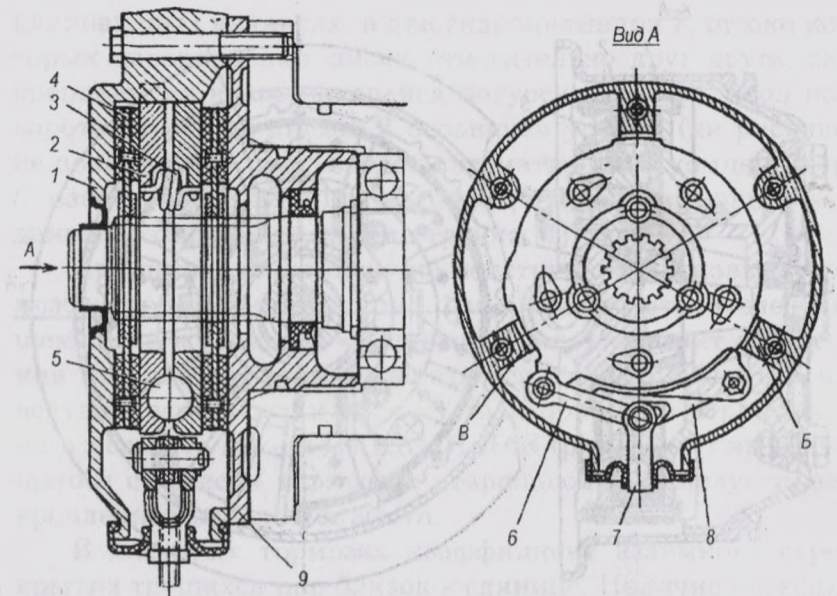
Дисковый тормоз трактора МТЗ-80: 1 – корпус тормоза; 2 – нажимной диск; 3 – пружина; 4 – тормозной диск с фрикционными накладками; 5 – шарик; 6 – тяга; 7 – вилка; 8 – тяга; 9 – крышка заднего моста
